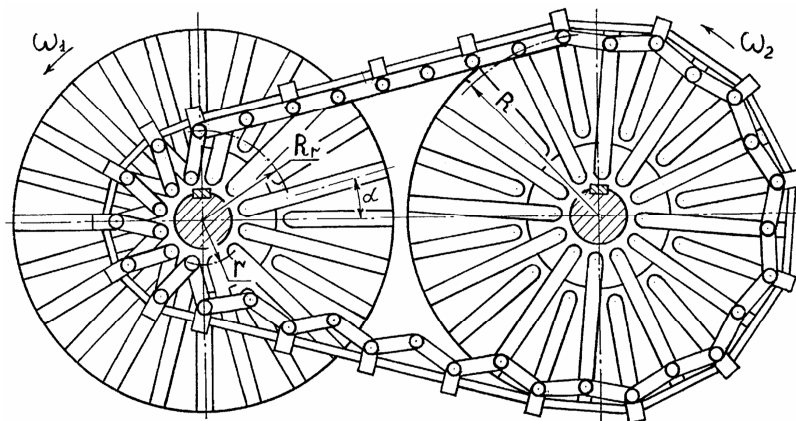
Схема зубчатого вариатора Б.В. Пылаева
